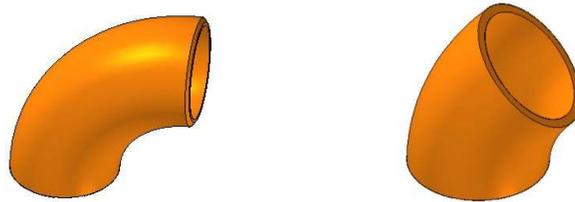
Conexiones tipo soldadura a tope
